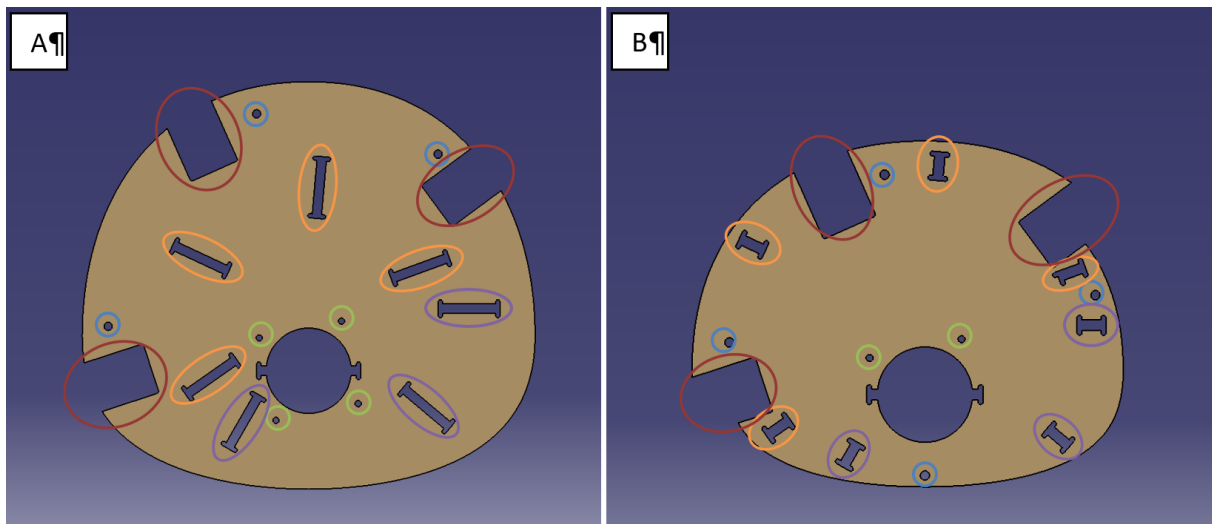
Bild A: Draufsicht des hinteren Hauptspanträgers; Bild B: Draufsicht des vorderen Hauptspanträgers.
